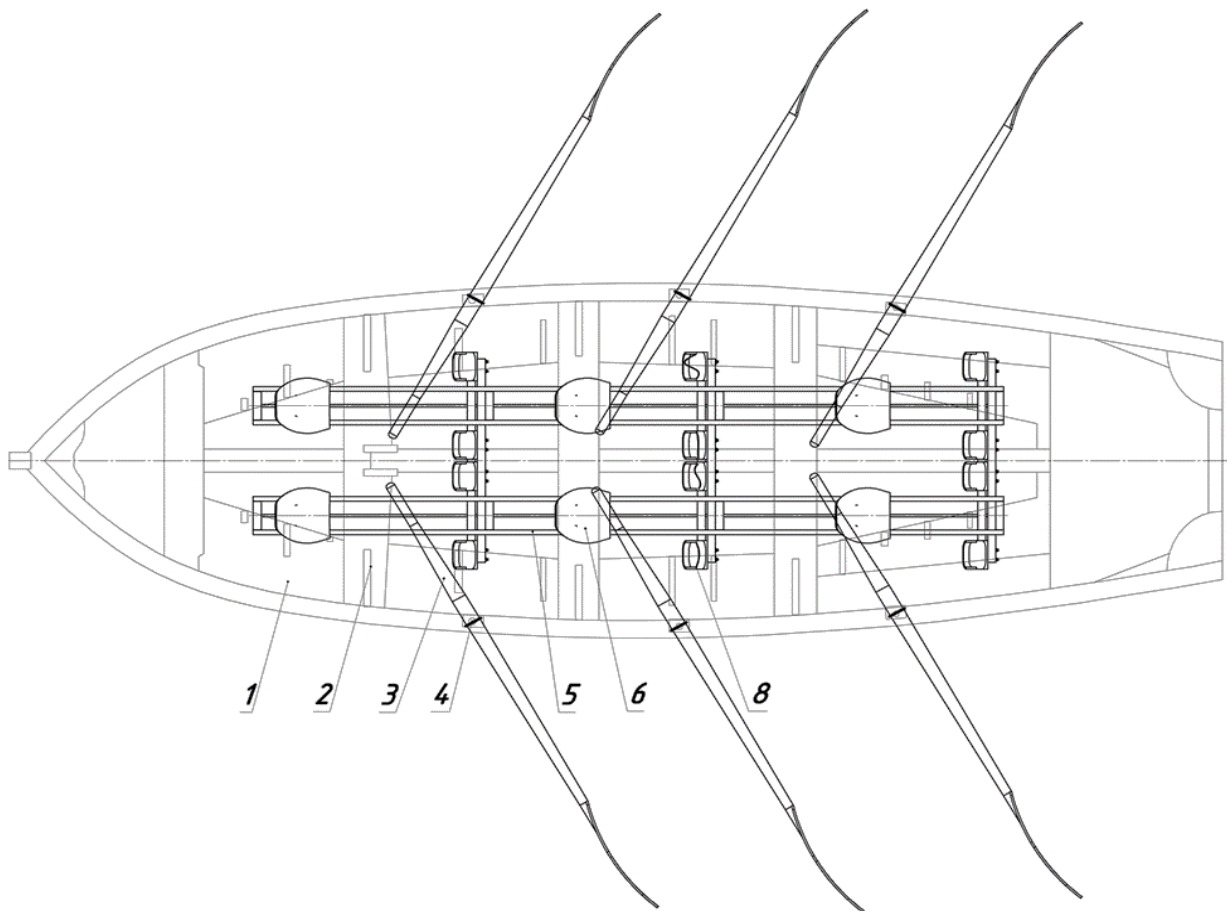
Гребное судно с установленной на нем подкатной системой (общий вид). 1 - корпус; 2 - банка; 3 - весло; 4 - уключина; 5 - направляющая; 6 - каретка; 8 - упор для ног
